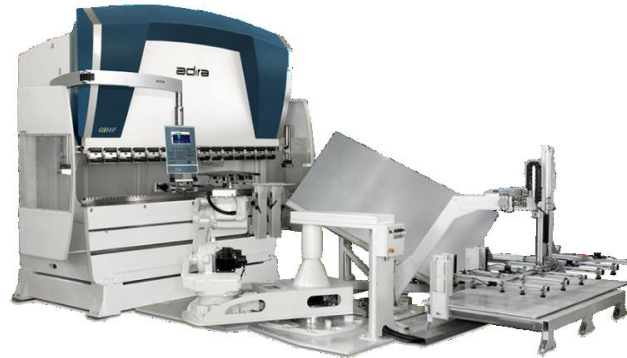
Célula de quinagem robotizada com alimentador de chapa (www.adira.pt)
